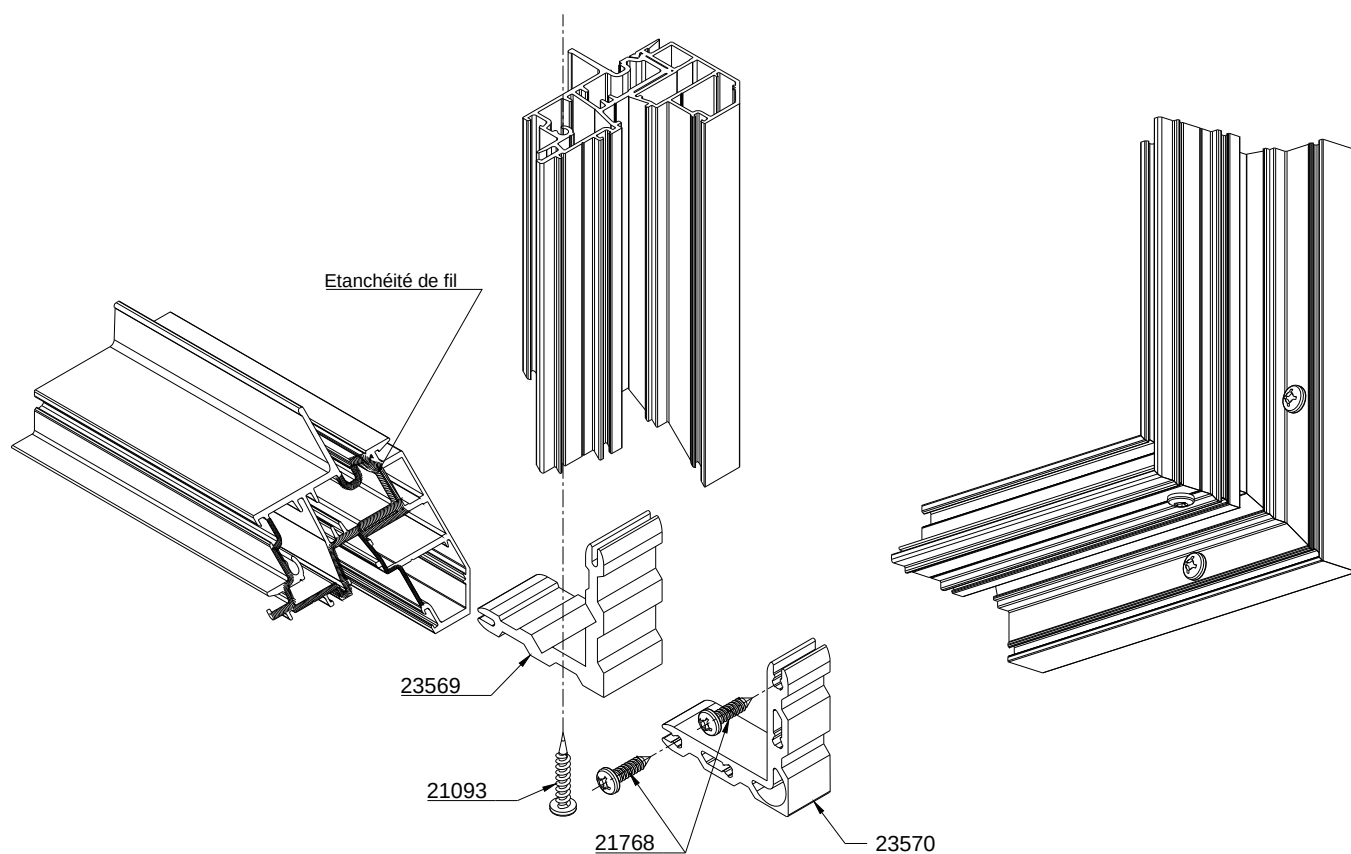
DETAILS D'ASSEMBLAGE ET ETANCHEITE SEUIL
